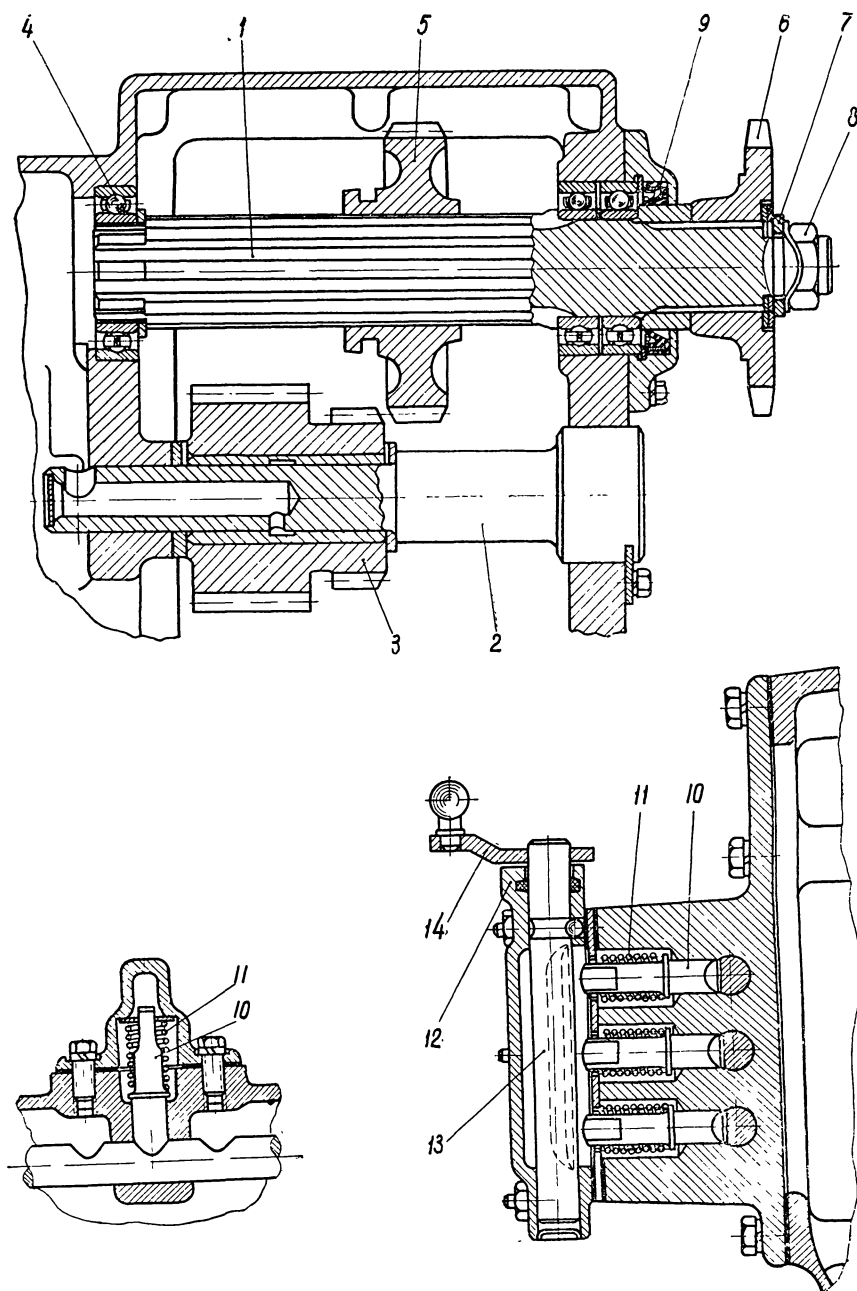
Коробка передач (привод на лебедку и механизм блокировки):
